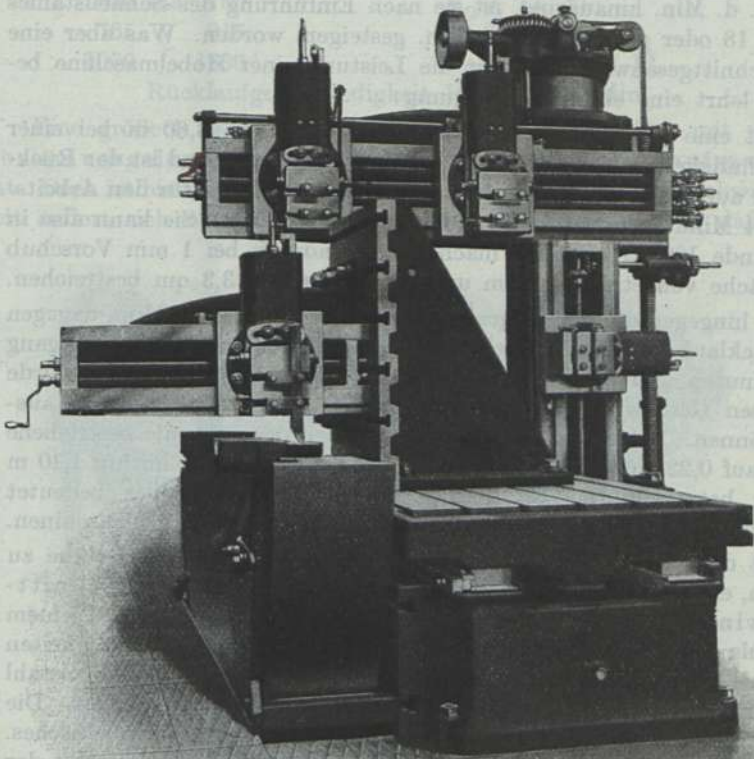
Einständer-Hobelmaschine mit Sondervorrichtung für das Hobeln von Schwungrädern. Billeter & Klunz, Aschersleben.
